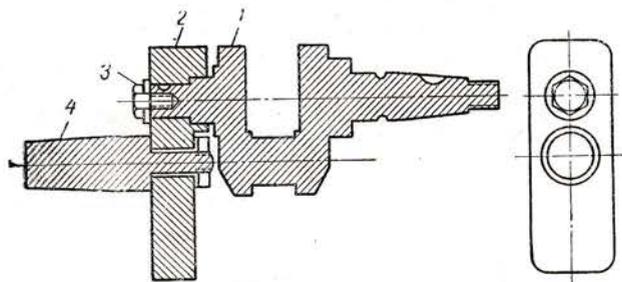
Общий вид приспособления для обточки коленчатого вала J1-3/2
